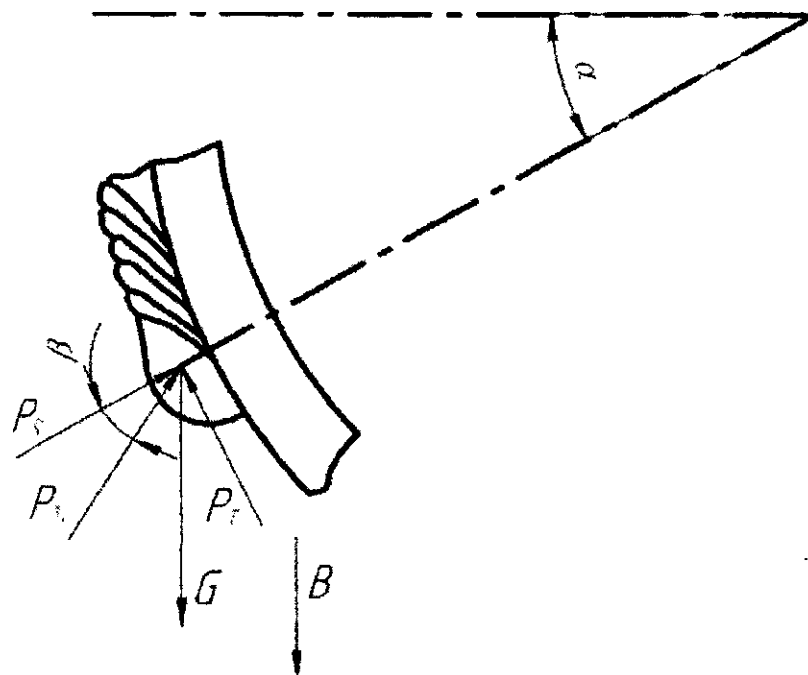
Схема сил действующих на сварочную ванну в положении от 90° - 180°
